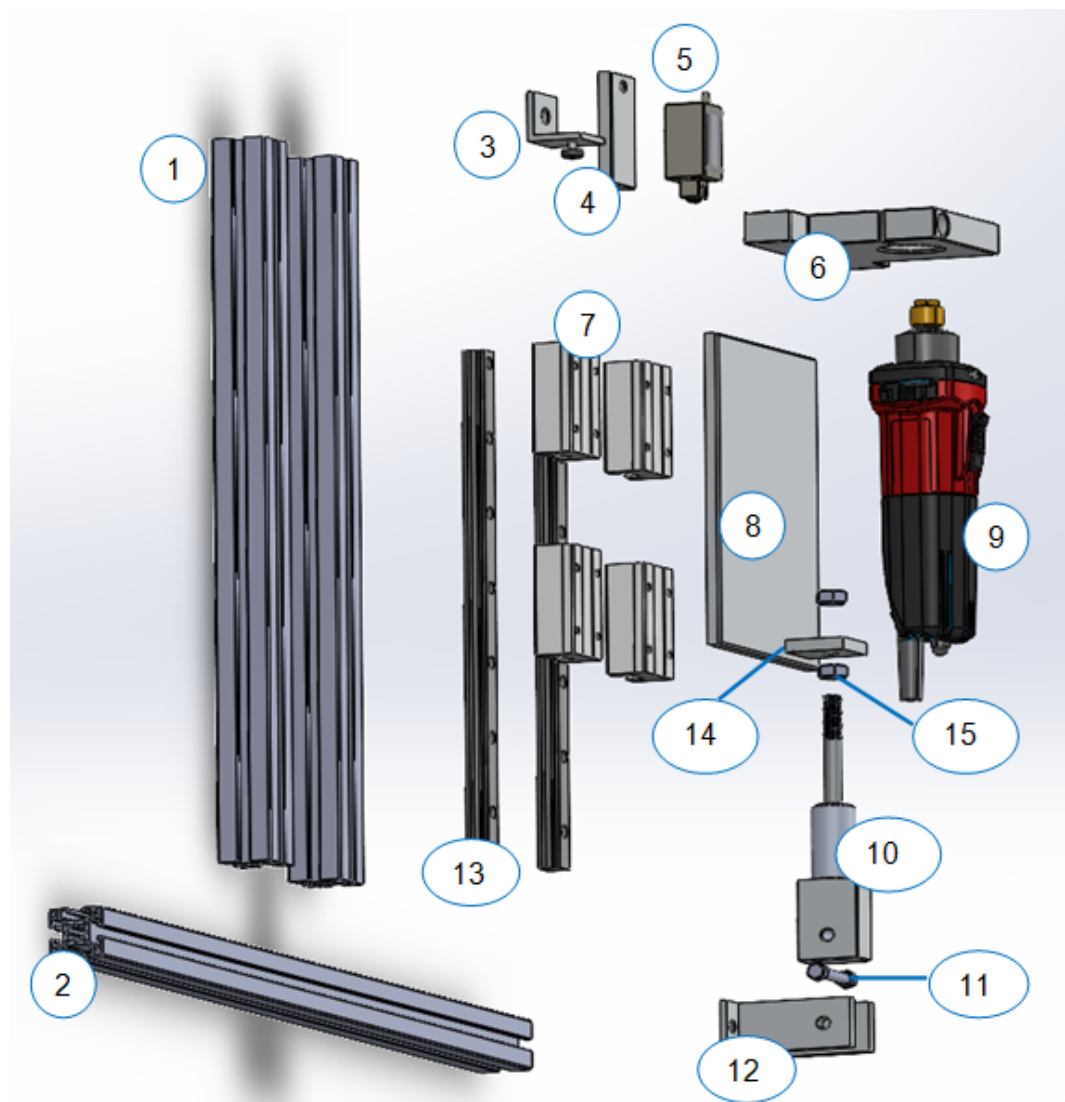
Baugruppe Antriebsmechanik Komponenten
